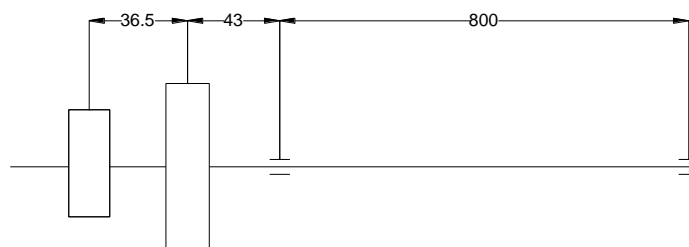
Elementos y su disposición de árbol excéntrico.
